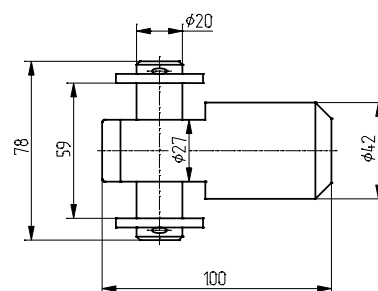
Соединительная тяга для механизмов МЗО-1600-92К (КБ) (в комплекте - вилка и шток)
